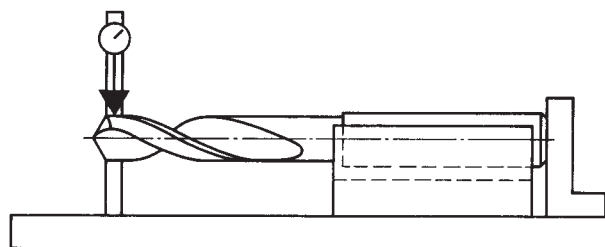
Prüfung des Rundlaufs bei Spiralbohrern mit Zylinderschaft
